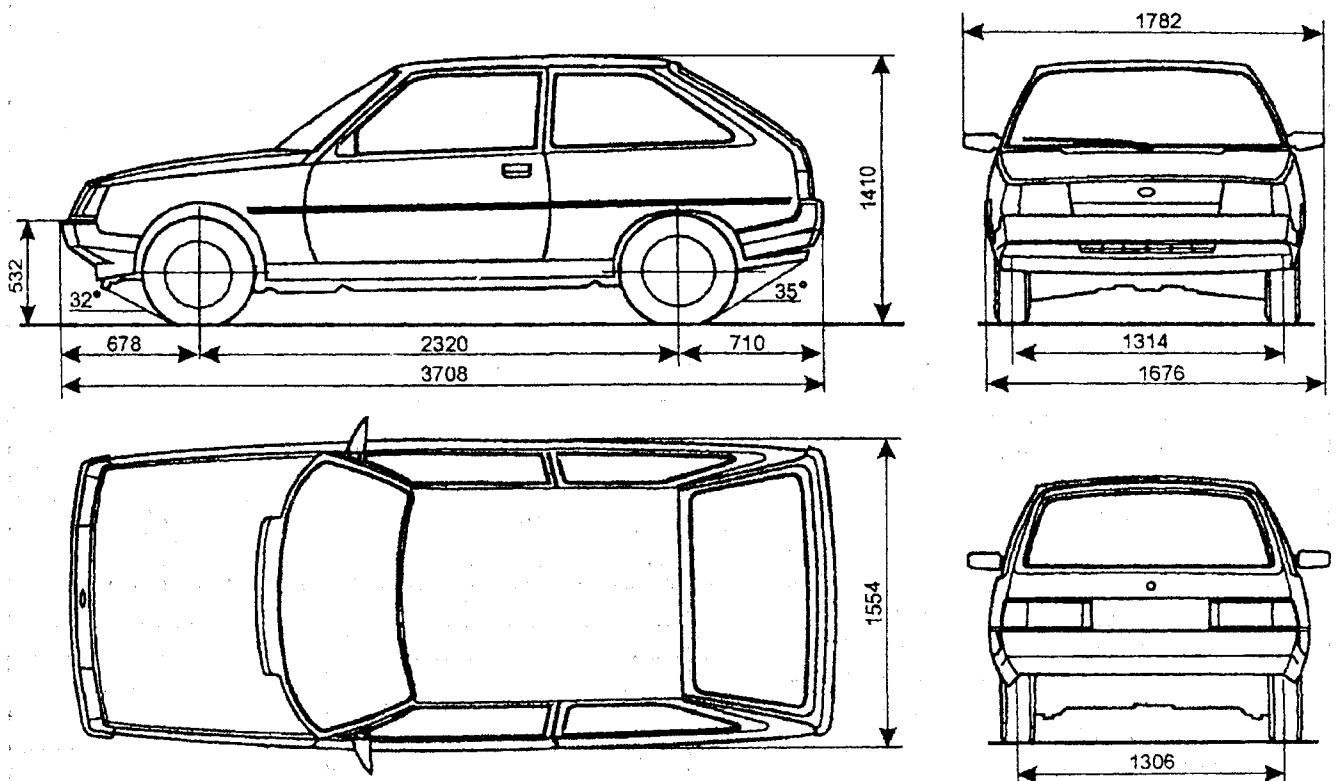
Основные габаритные размеры автомобилей ЗАЗ-110206, ЗАЗ-110216 (высота без нагрузки)
